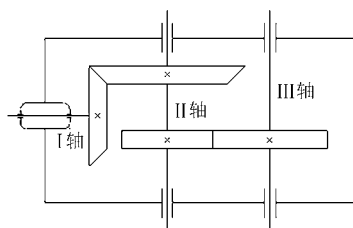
两级圆锥-斜齿圆柱齿轮减速器设计方案简图
